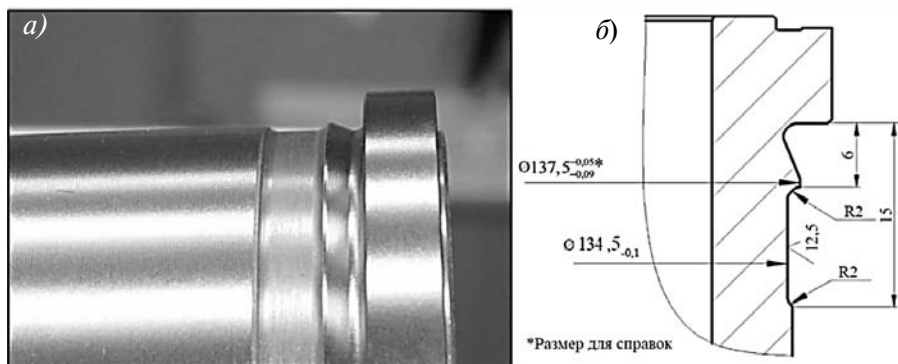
Внешний вид гильзы цилиндра с доработкой зоны верхнего посадочного пояса (а) и эскиз доработки гильзы цилиндра (б)
